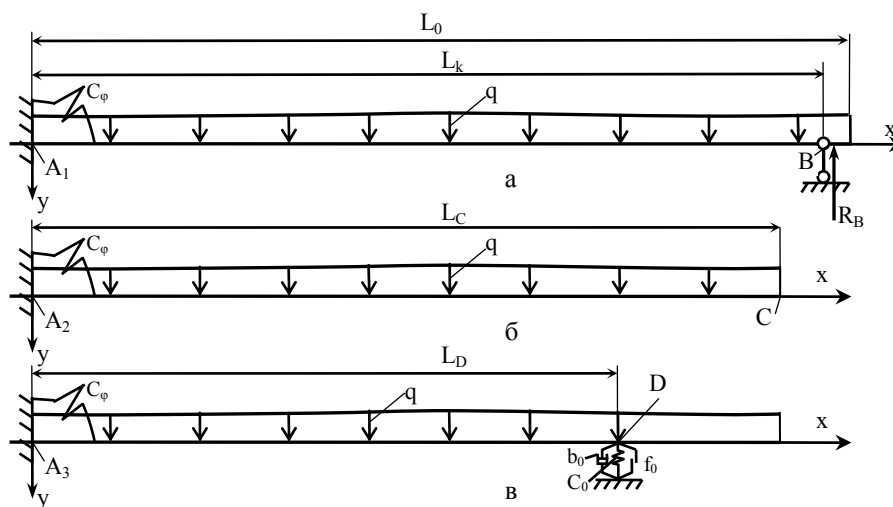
Зміна умов опирання і закріплення заготовки, яка має місце при роботі верстата: а – опирання кінцевої частини заготовки на кільце; б – консольне закріплення заготовки; в – введення проміжної пружно-демпфуючої опори заготовки
